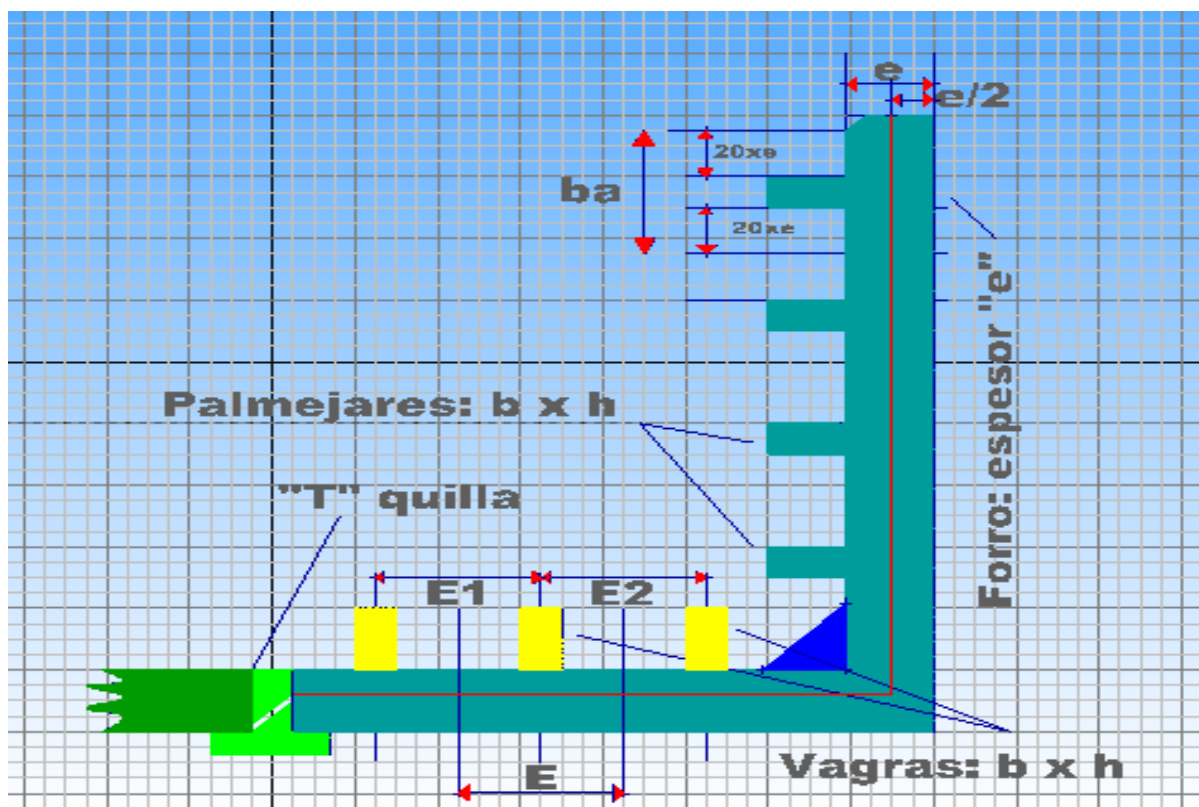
Vista transversal de un fondo de casco...
